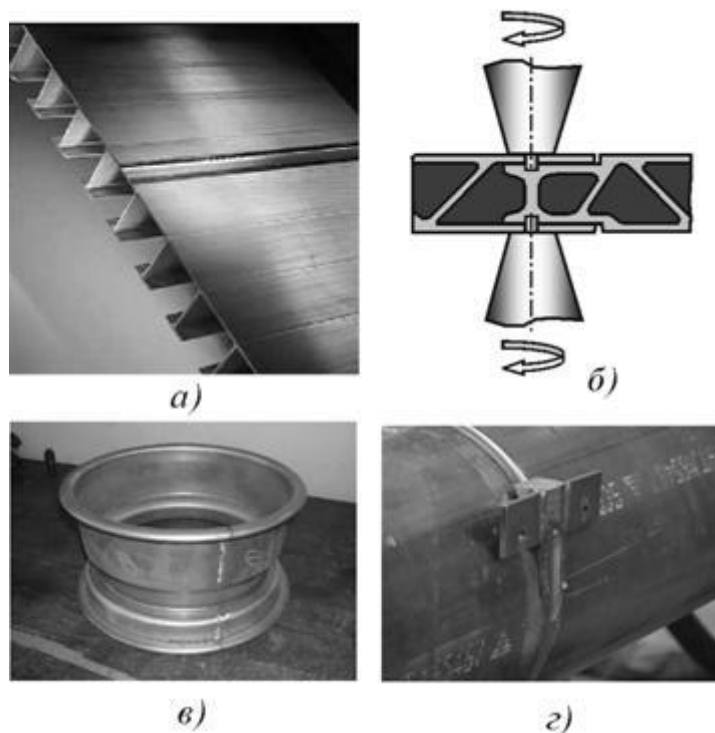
Изделия, сваренные ПСТ: а – панель; б – схема двухсторонней сварки панели; в – деталь в виде оболочки; г – труба
